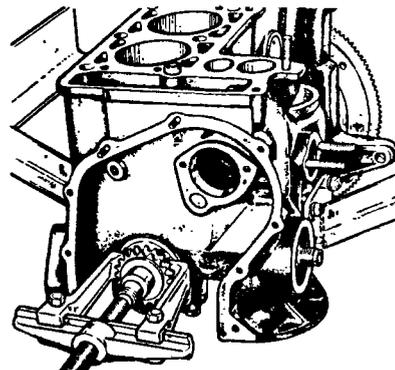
Снятие звездочки коленчатого вала универсальным съемником А.40005/1/7
